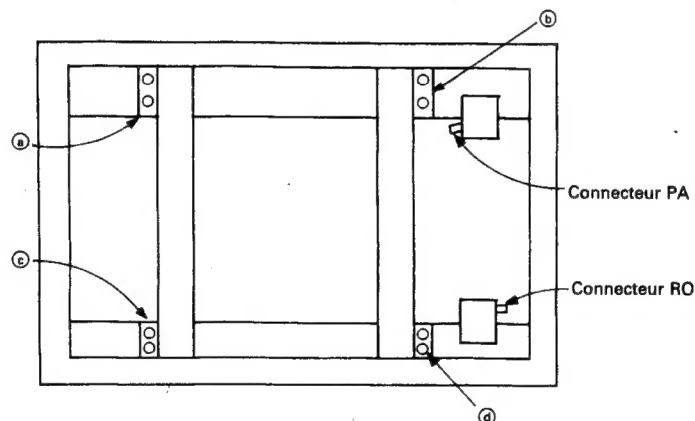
Unité de mécanisme de rotation (couvercle arrière démonté)
